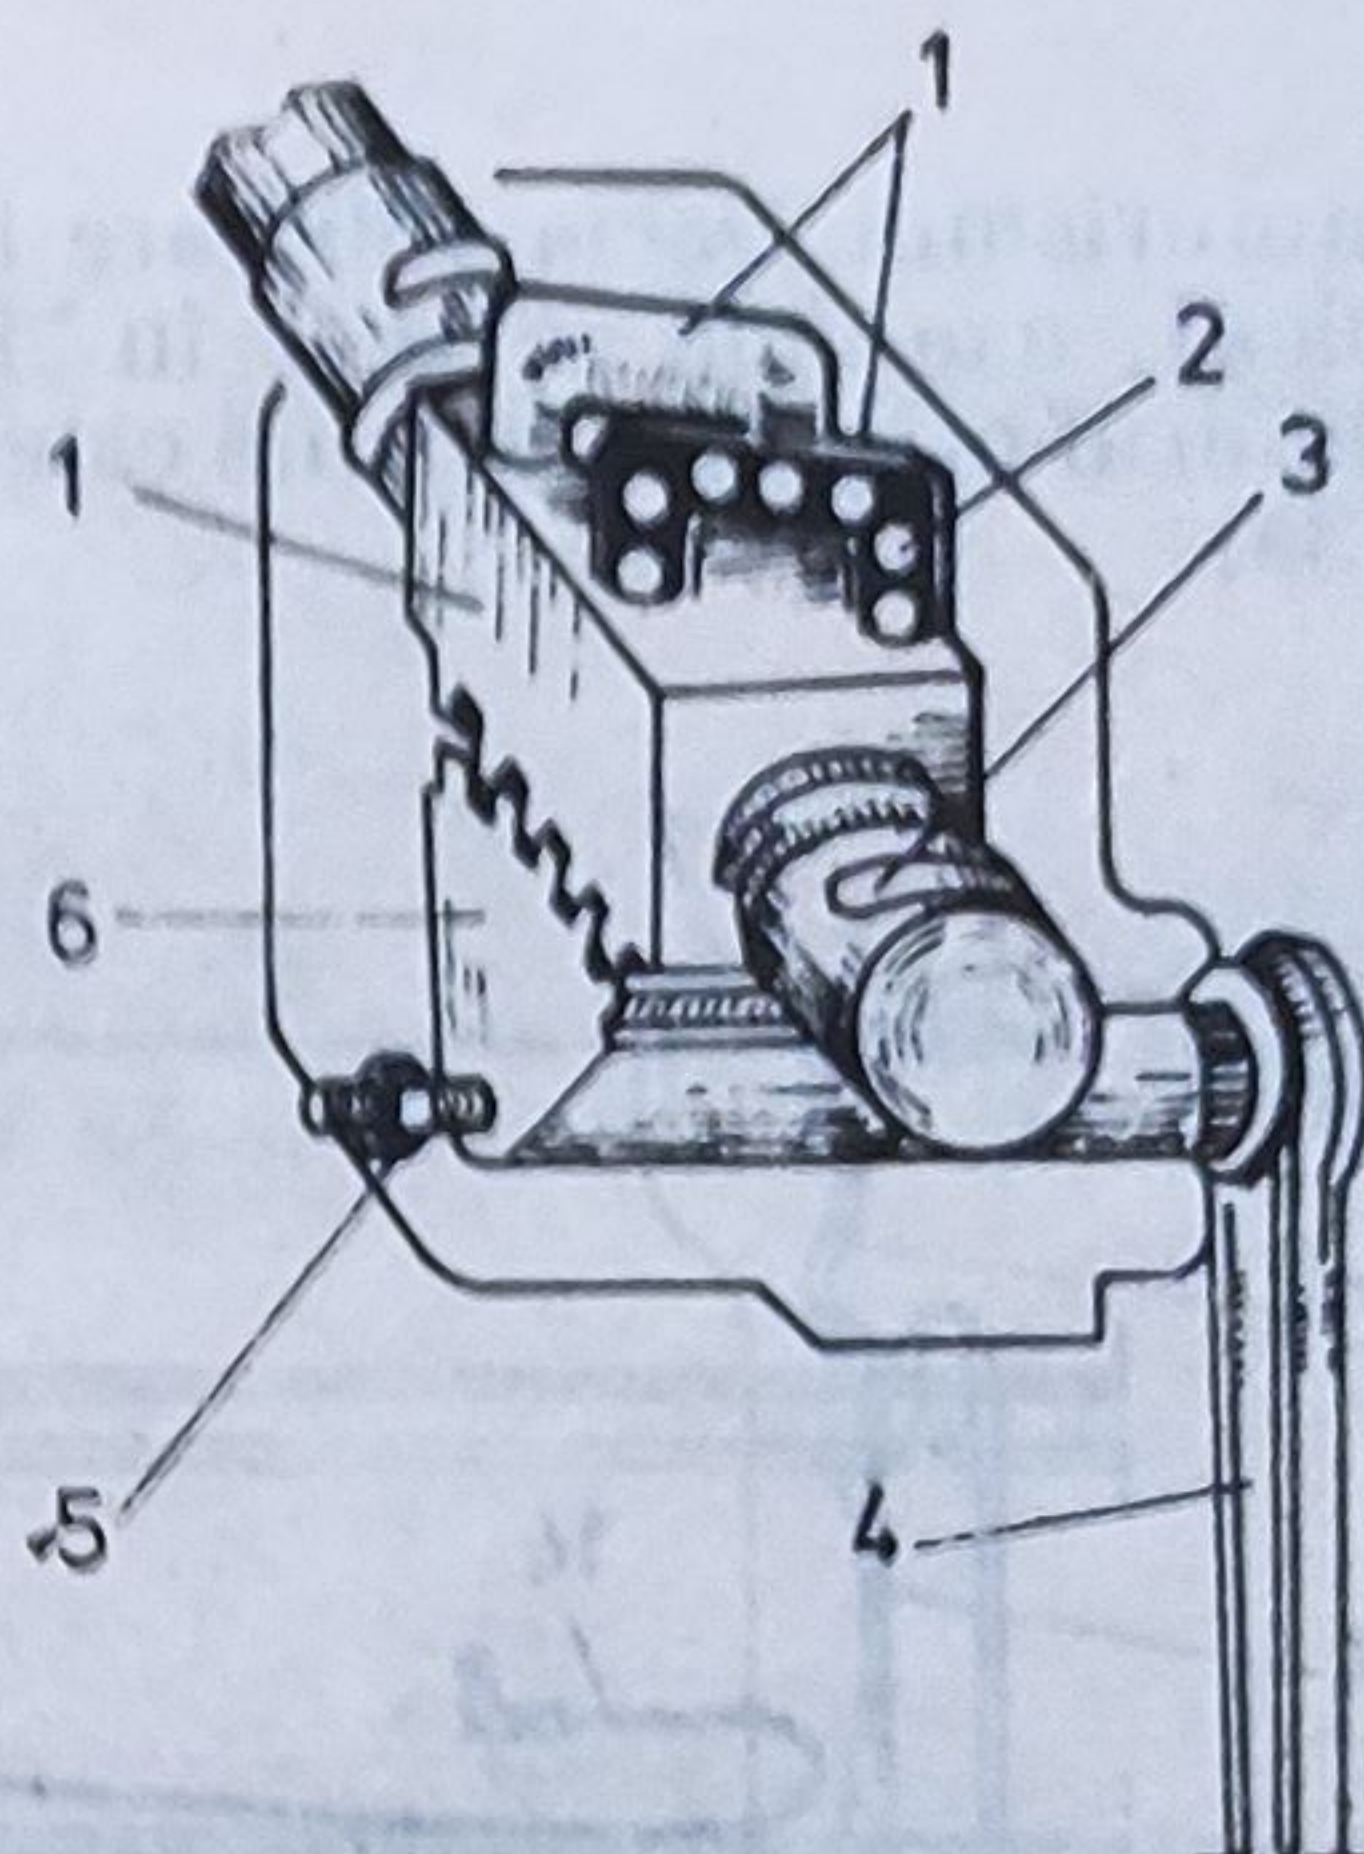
Mecanismul de direcție cu șurub, bile recirculante, piulița și sector dîntat; 1 — tub de ghidare; 2 — bile; 3 — șurub; 4 — levier de comandă; 5 — șurub de reglaj; 6 — sector dîntat; 7 — piulița cu cremalieră la exterior.
